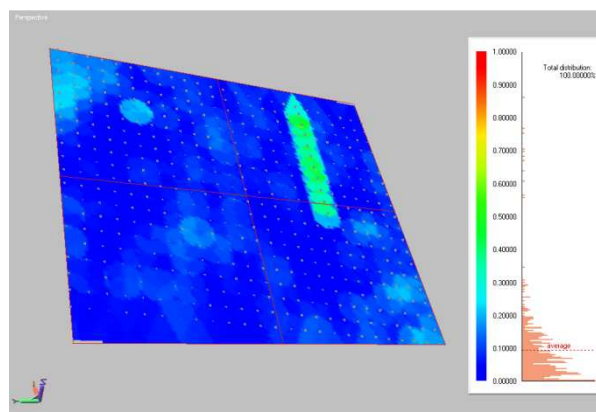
Déviation entre le nuage de points mesuré sur un plan en acier et un plan parfait
